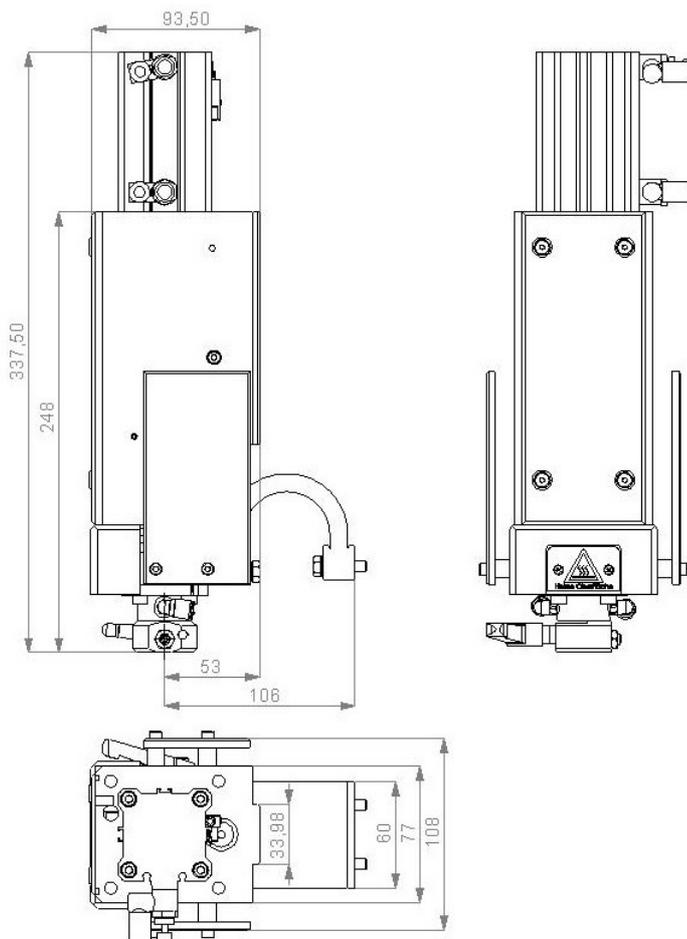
Abmessungen Schweißkopf SK-2110 (ohne Schweißkopfständer)
